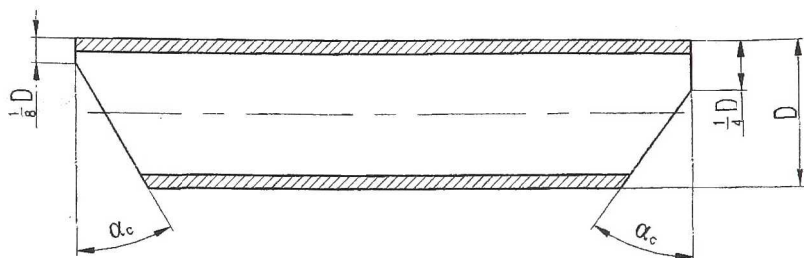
Форма заготовки для гибки крутоизогнутого патрубка проталкиванием на угол $\beta = \pi/2$
